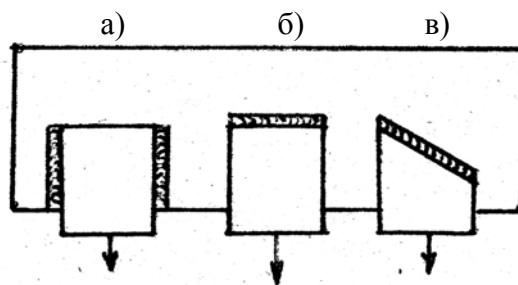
Зварні шви: а) флангові; б) лобові; в) косі
